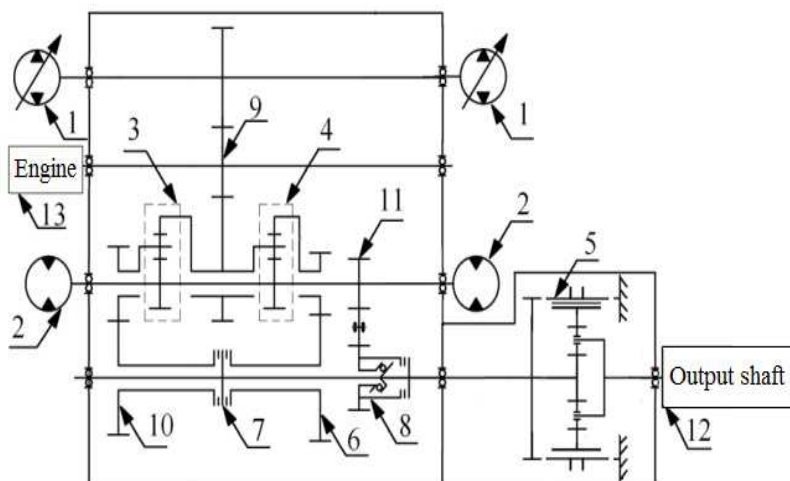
Кінематичні схеми трансмісій ГОМТ: 1 – регульований гідронасос; 2 – нерегульований гідромотор; 3, 4, 5 – планетарні механізми; 6, 9, 10, 11 – редуктори; 7 – гідропідтисні муфти; 8 – обгінна муфта; Engine – двигун внутрішнього згоряння; Output shaft – вихідний вал.
